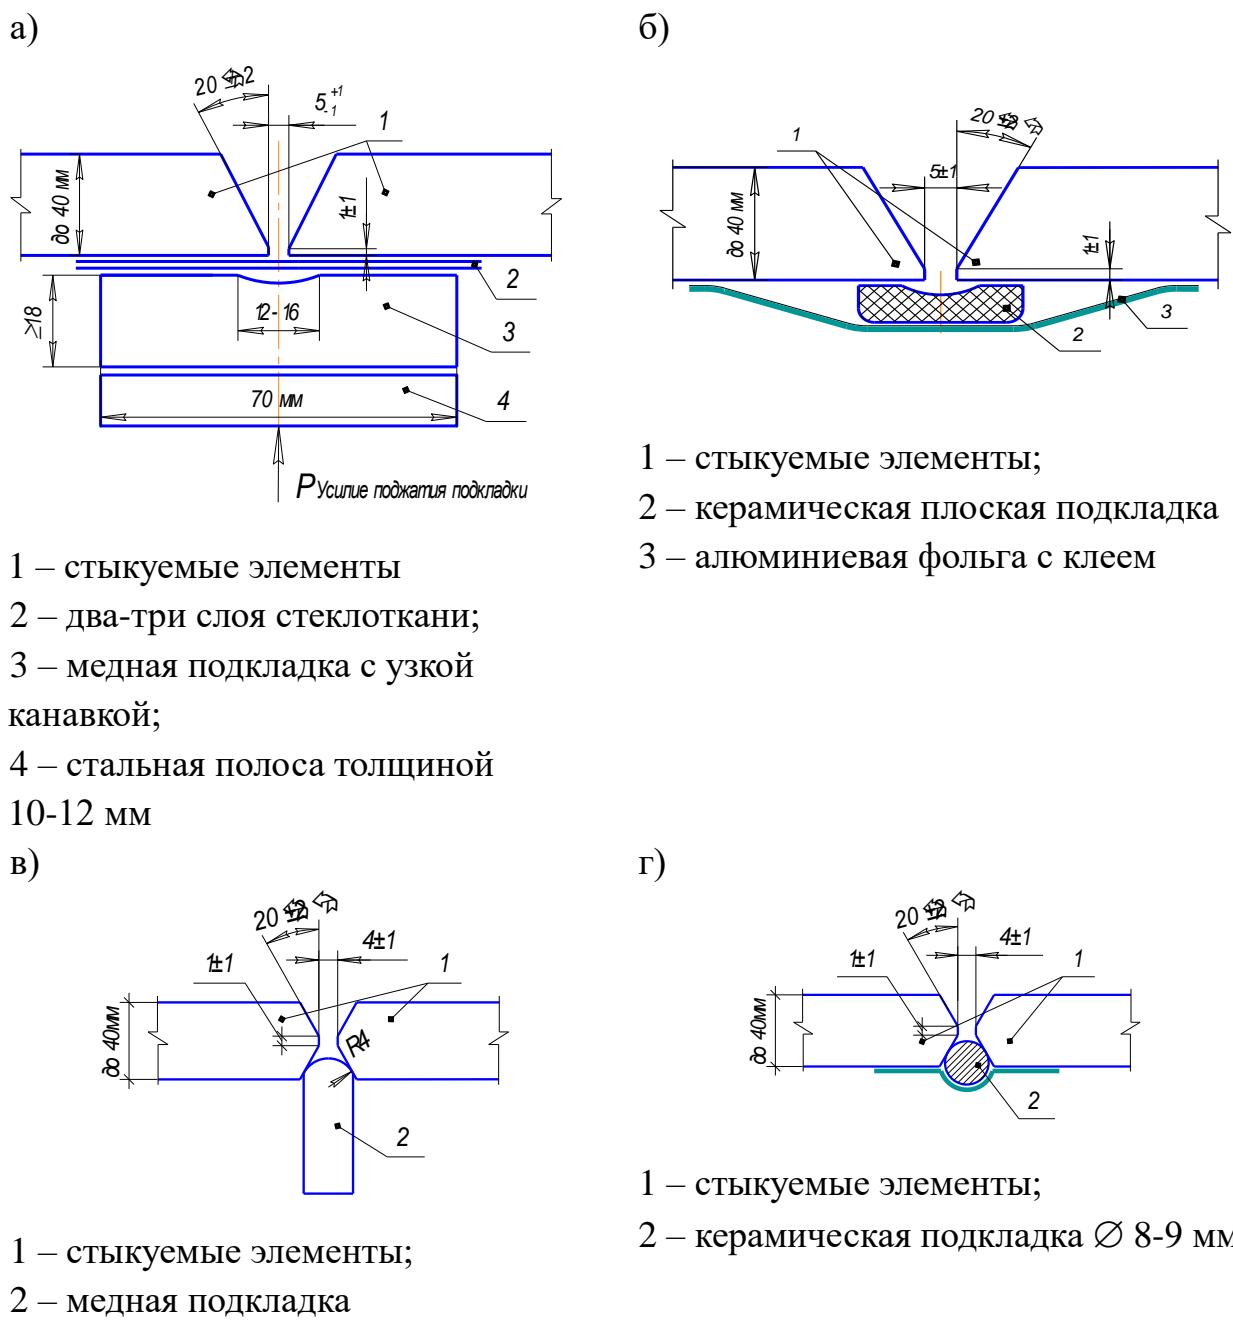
Схемы сборки монтажных стыковых соединений под механизированную сварку порошковой проволокой в смеси защитных газов (МПГ)
